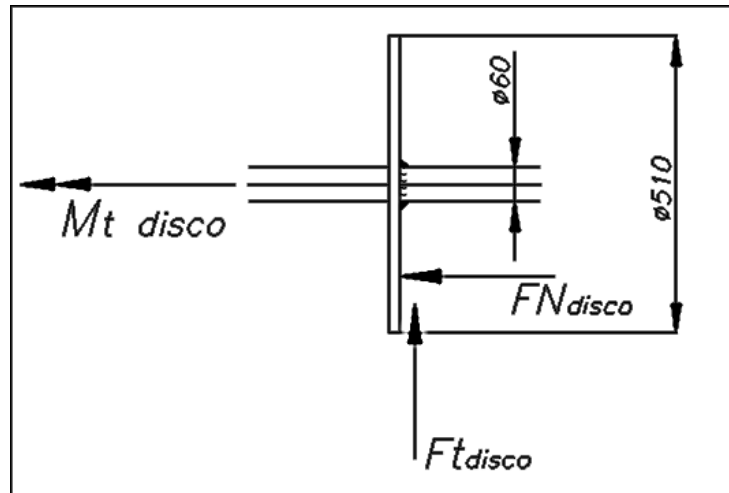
Unión soldada entre disco idealizado y árbol del transportador
